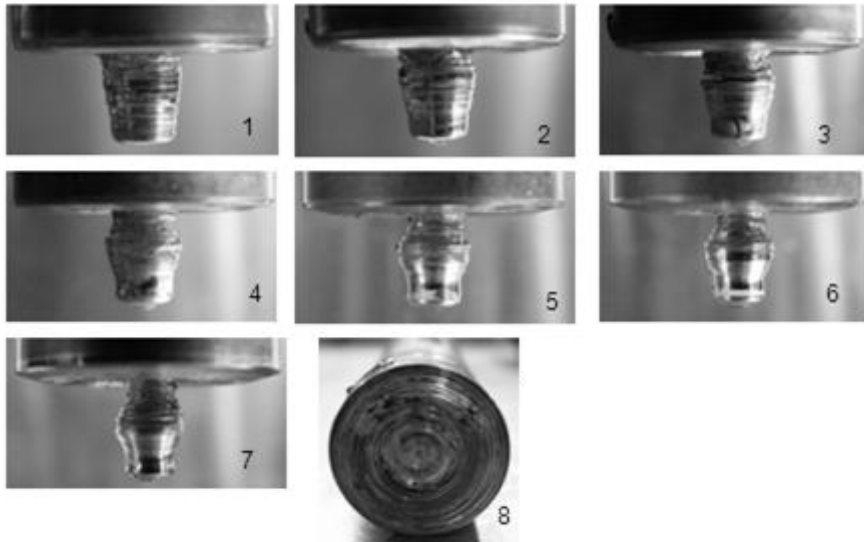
Aspecto de la herramienta al finalizar cada pasada de 220 mm de largo en 25%SiC/2124Al a 700 rpm y 75 mm/min.
